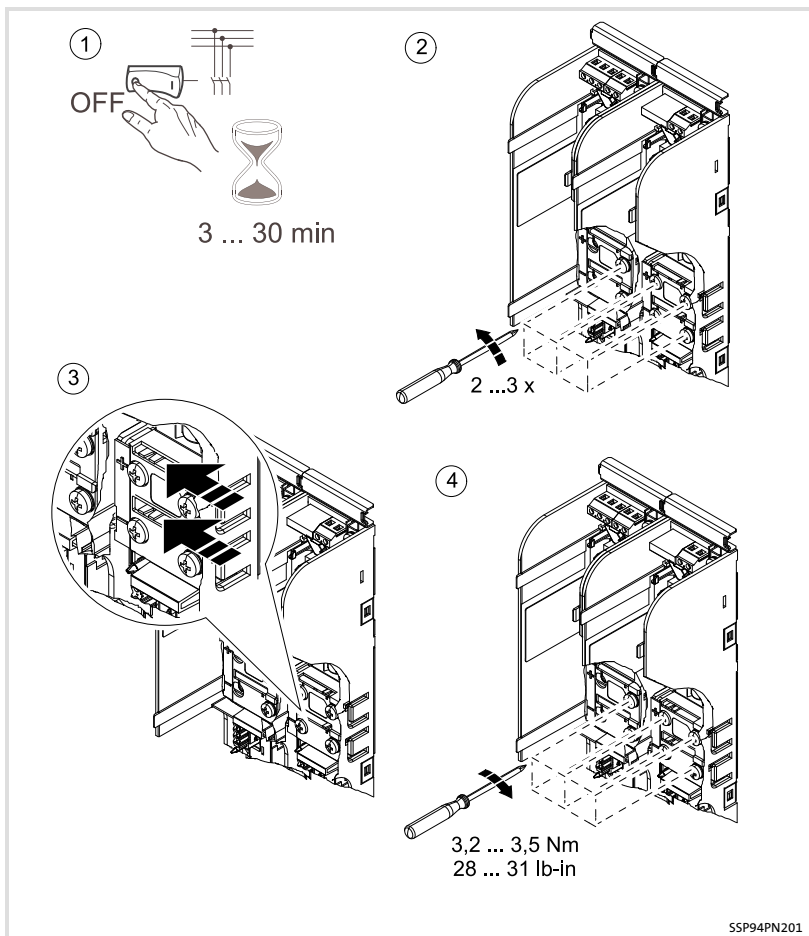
Esempio: collegamento delle sbarre DC bus
